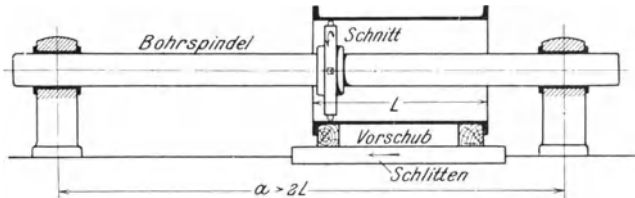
Zylinderbohrmaschine mit wanderndem Tisch.
